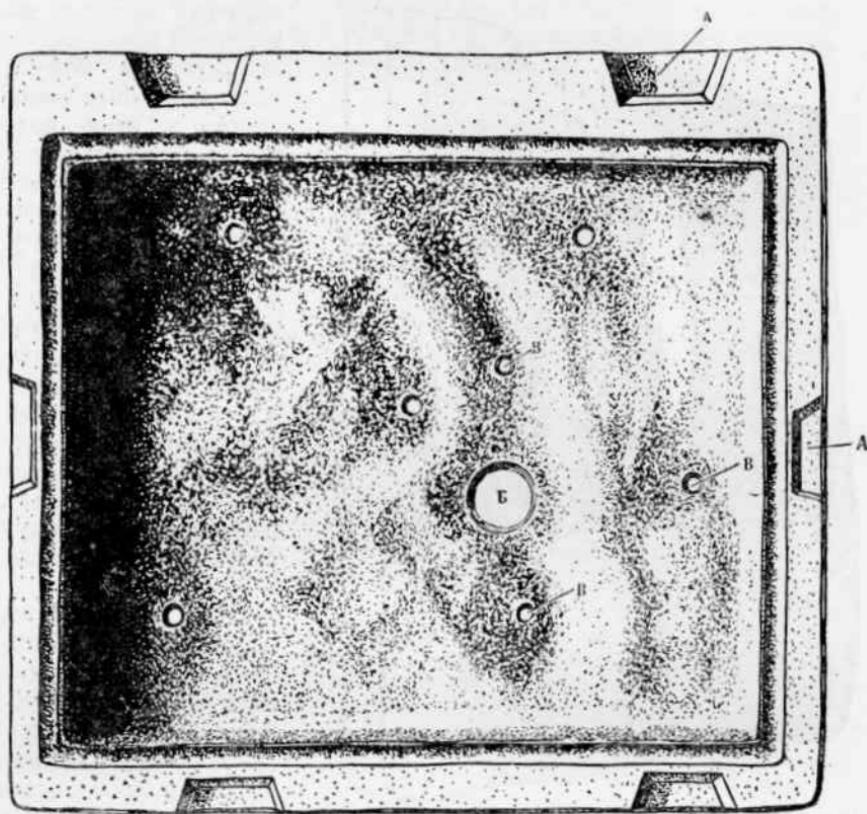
Клеевая формовка сложного рельефа. Изготовление кожуха. Кожух: А — места для замков, Б — большое отверстие для вливания клея, В, В, В — малые отверстия для выхода воздуха из кожуха при наливке клея.
